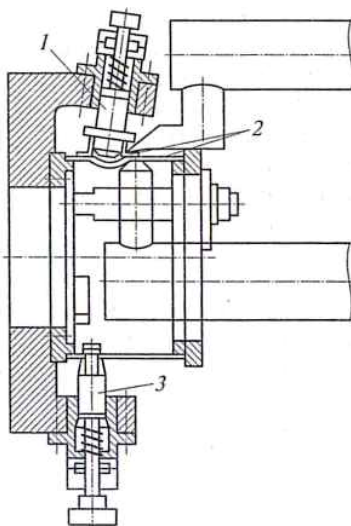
Кондуктор для сборки и прихватки конусов: 1 и 8 – консоли;
